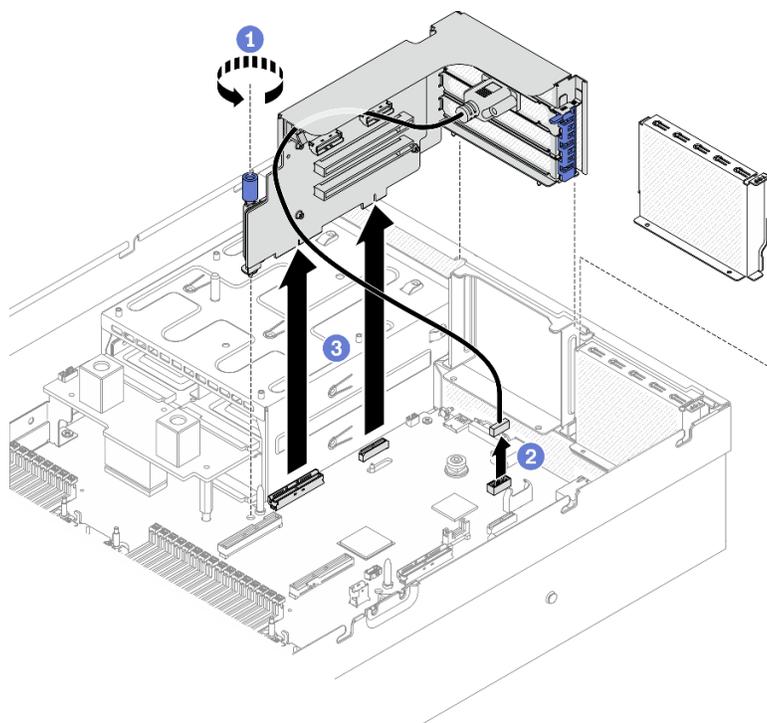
Removendo a placa riser PCIe 2 instalada com porta serial
